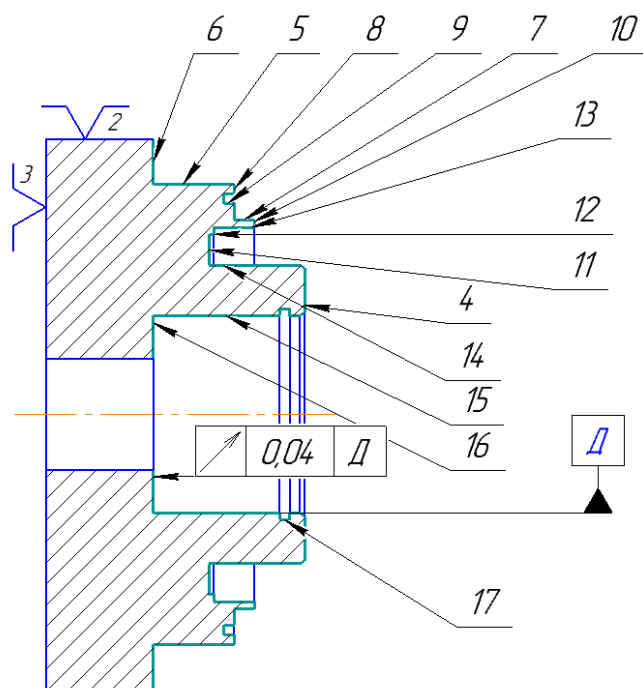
Эскиз токарной операции с ЧПУ, установ А
